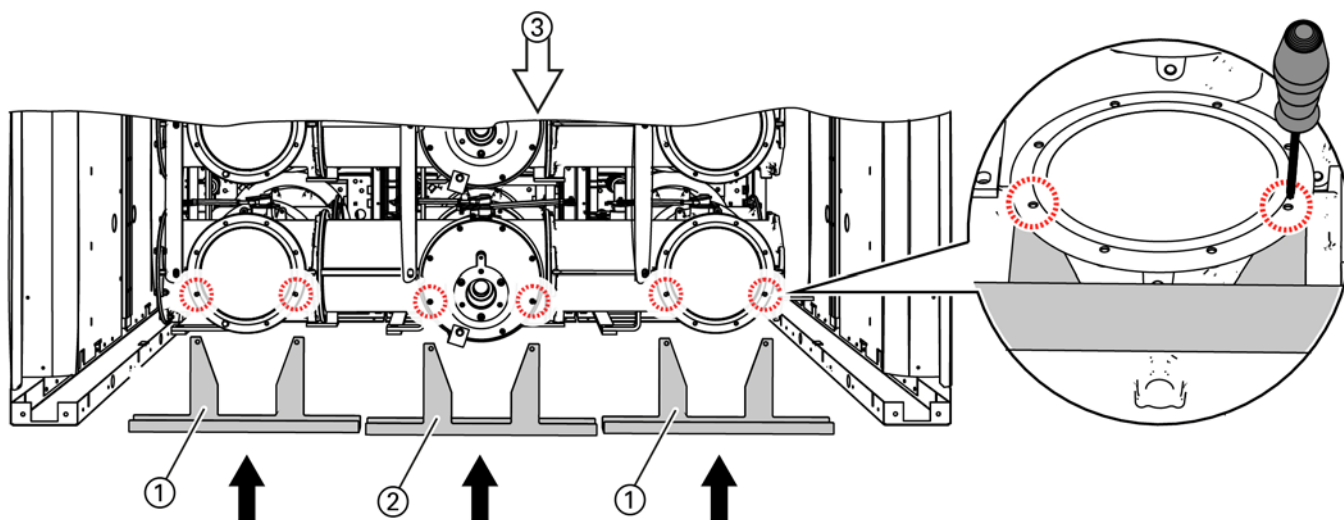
Смонтируйте крепежные траверсы на корпусах сборных шин
